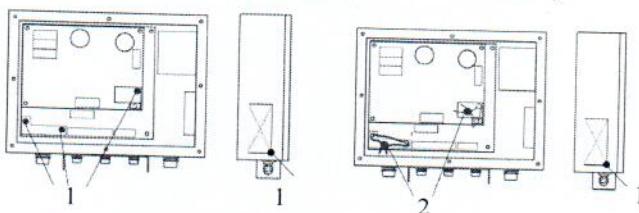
Схема пломбировки корпуса весоизмерительных приборов:
